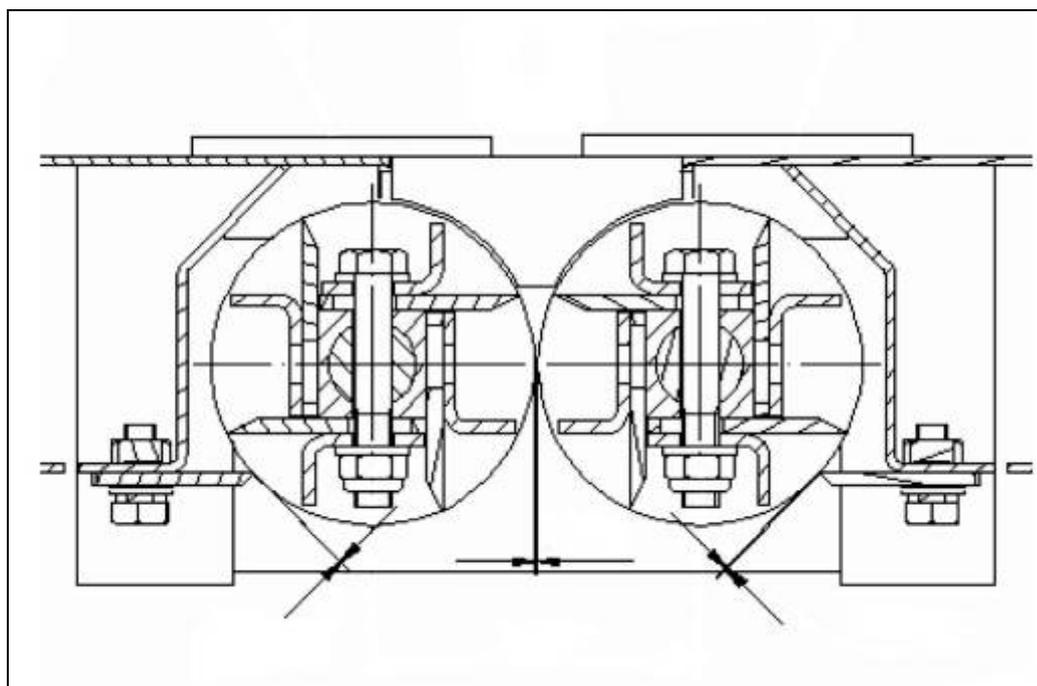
Режущие вальцы с четырьмя ножами и четырьмя дополнительными активными ребрами
